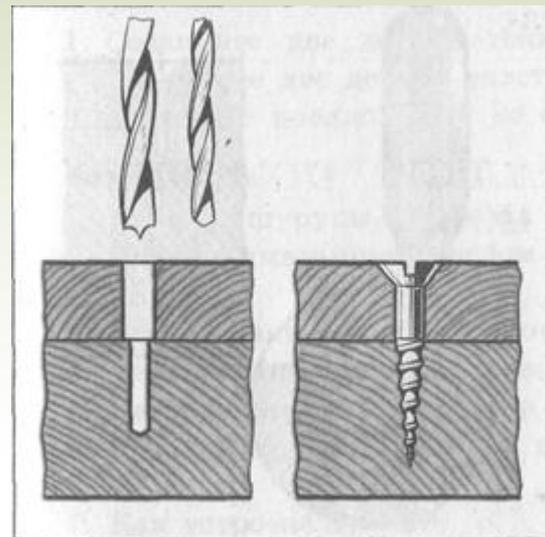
Сверление отверстия под шуруп двумя сверлами.
